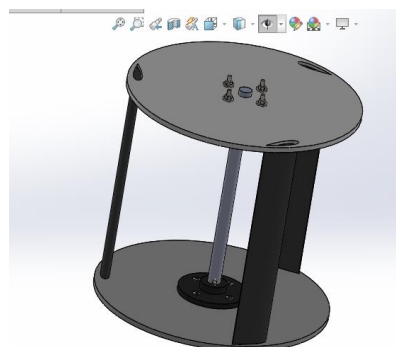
Ensamblaje turbina en software CAD, Fuente: Autor.
